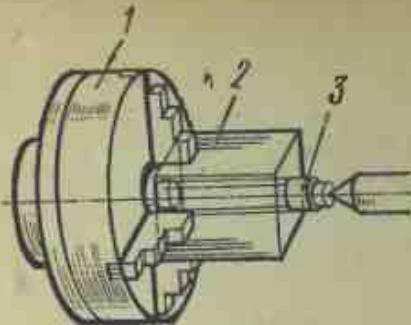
Установка заготовки в четырехкулачковом патроне с помощью цилиндрической опправки:
